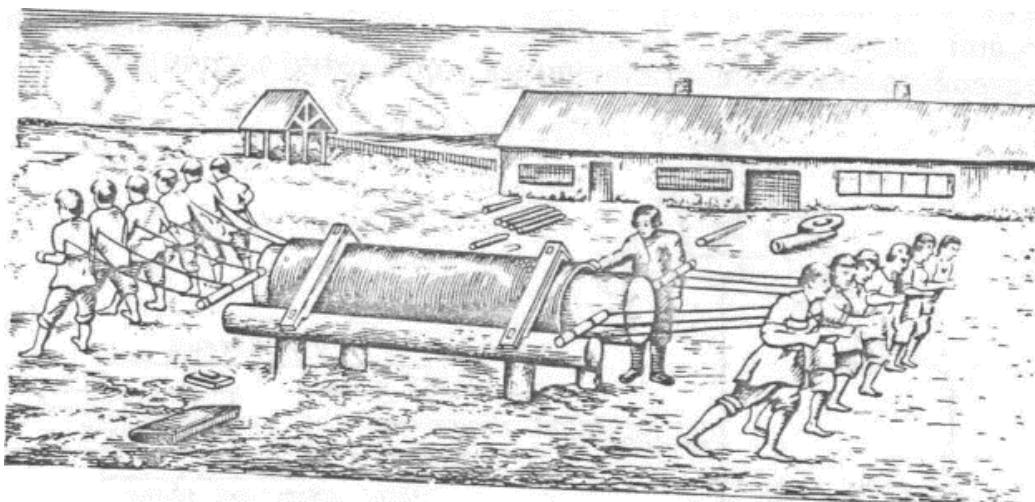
Шлифование металлического цилиндра, 1760 г.
